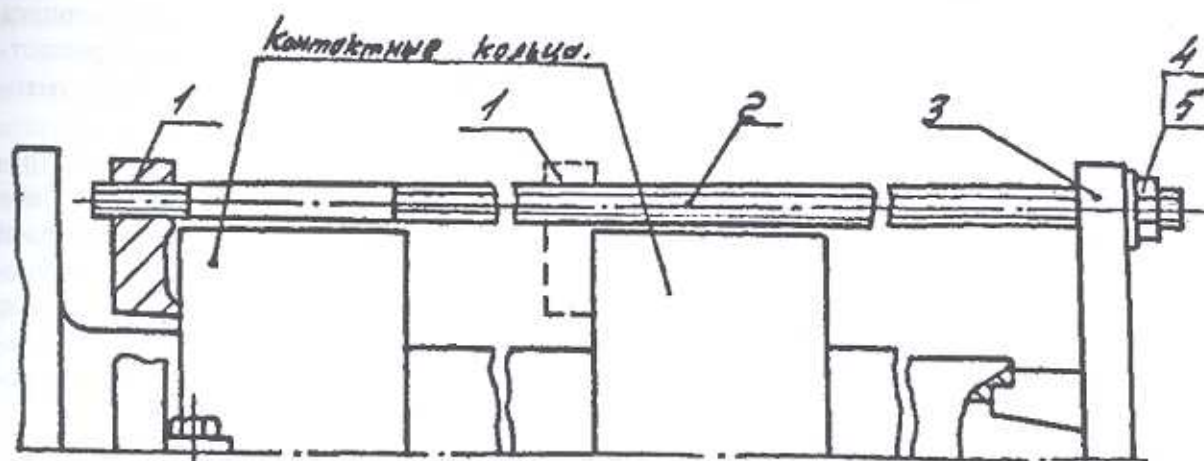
Установка приспособлений для снятия контактных колец ротора:
